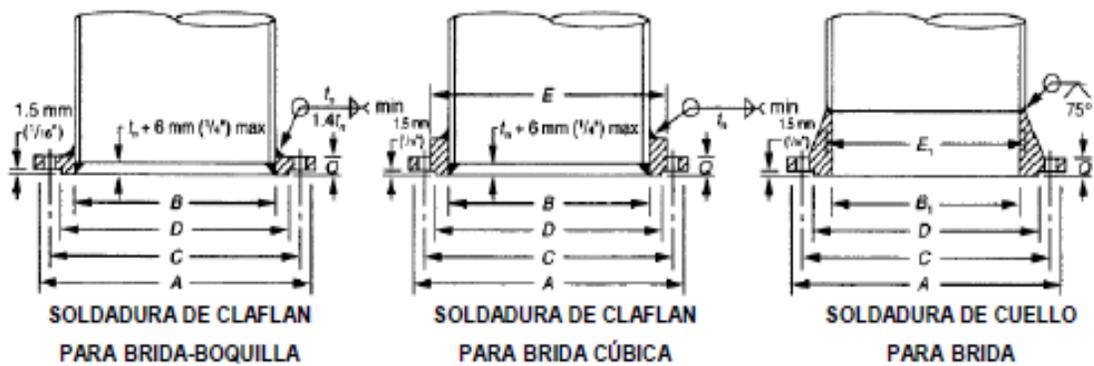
Tipos de soldadura para Bridas¹¹.
